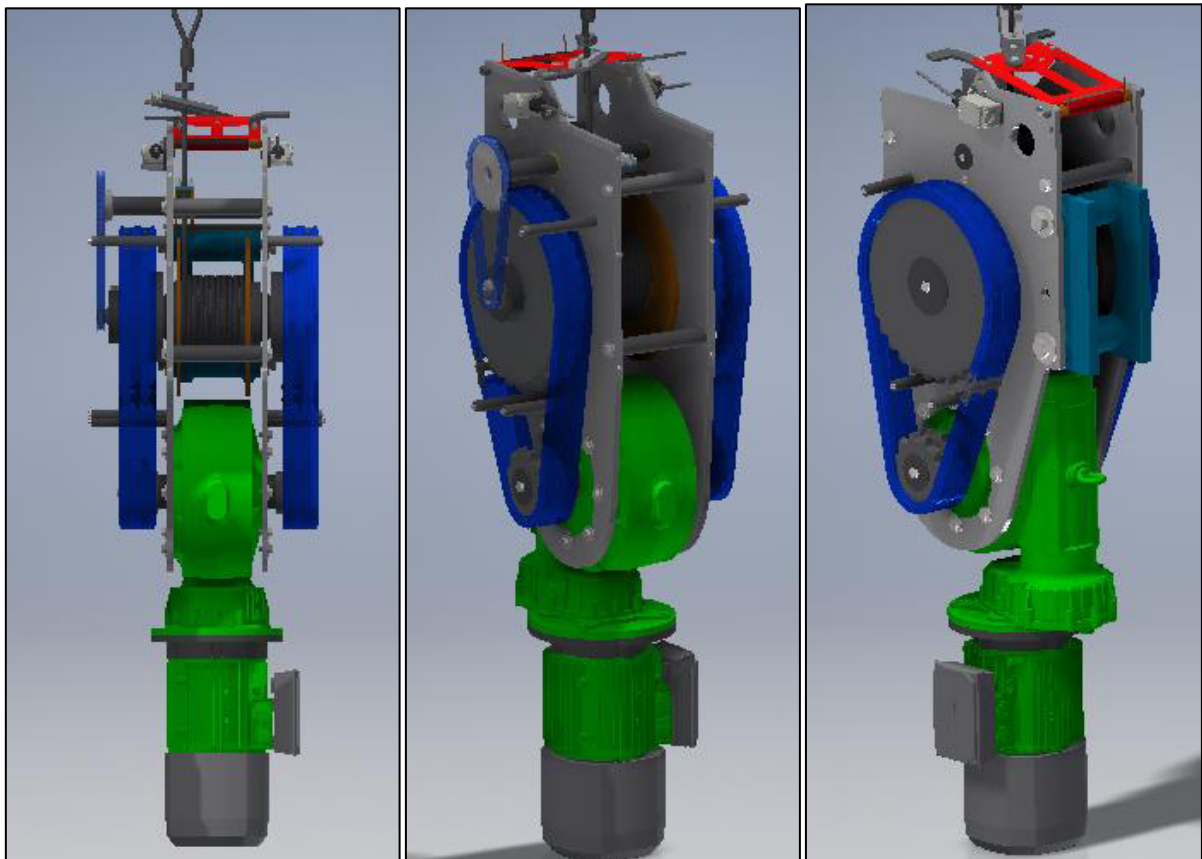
Desenho em CAD 3D do mecanismo sobe e desce 2000 kg (tampas frontal e laterais removidas).
